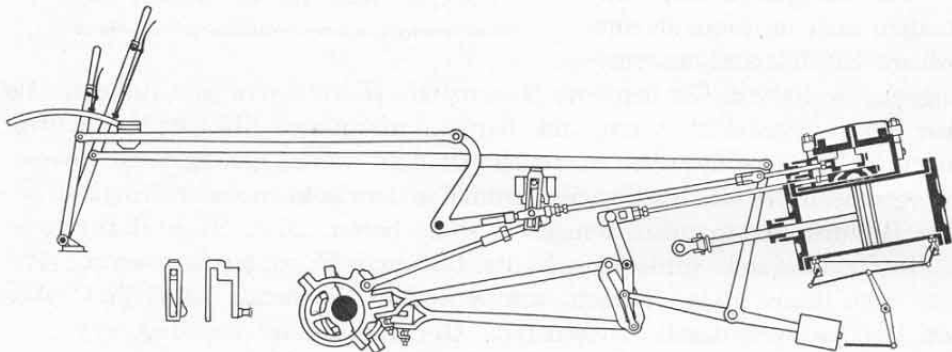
und 776. Expansionssteuerung von Borsig 1844.
